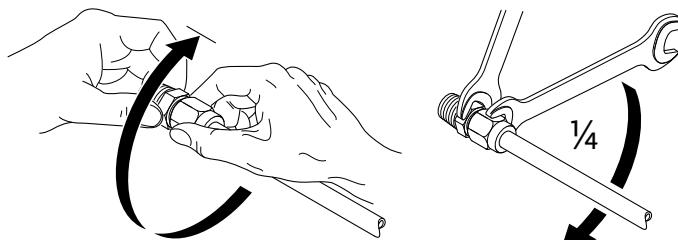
Допълнително завъртане на компресионния фитинг с $1/4$ оборот
